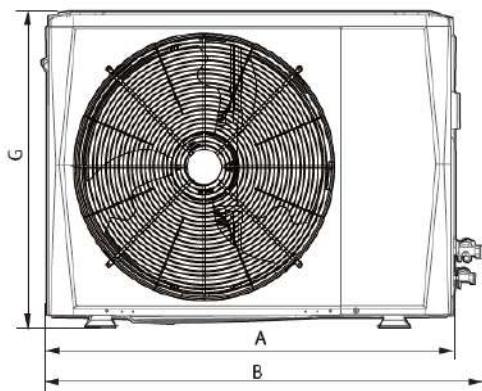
Dimensiones de la vista frontal del modelo 36-56
